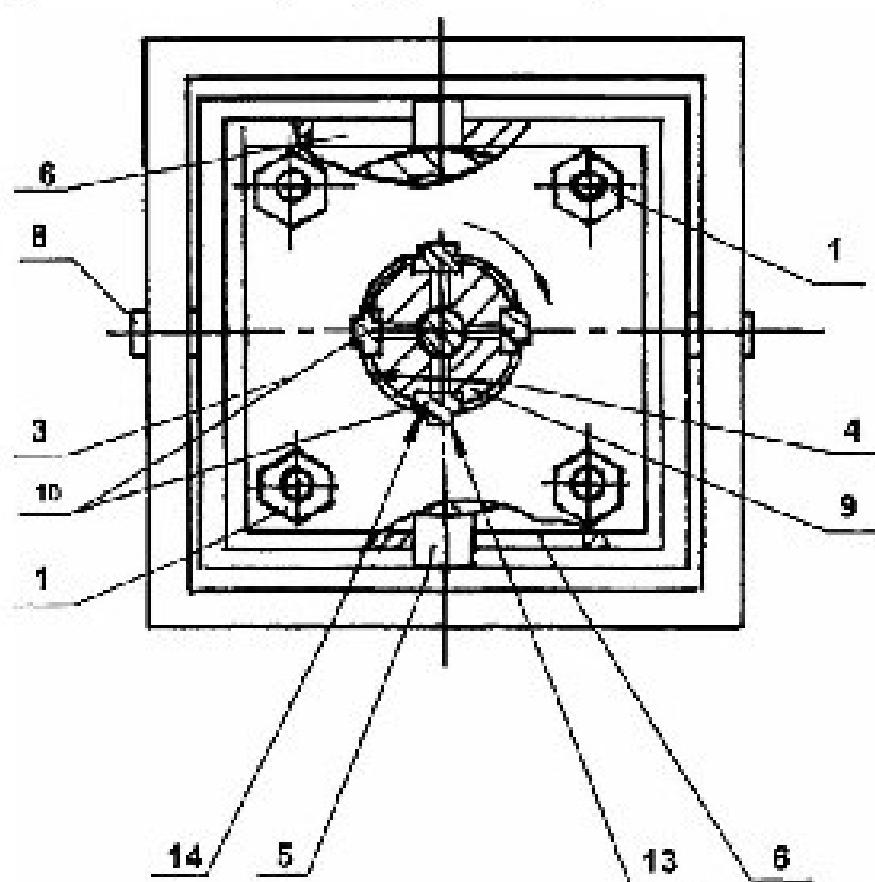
Устройство для финишной обработки полости гильзы цилиндра дсв (патент РФ 2482951)
